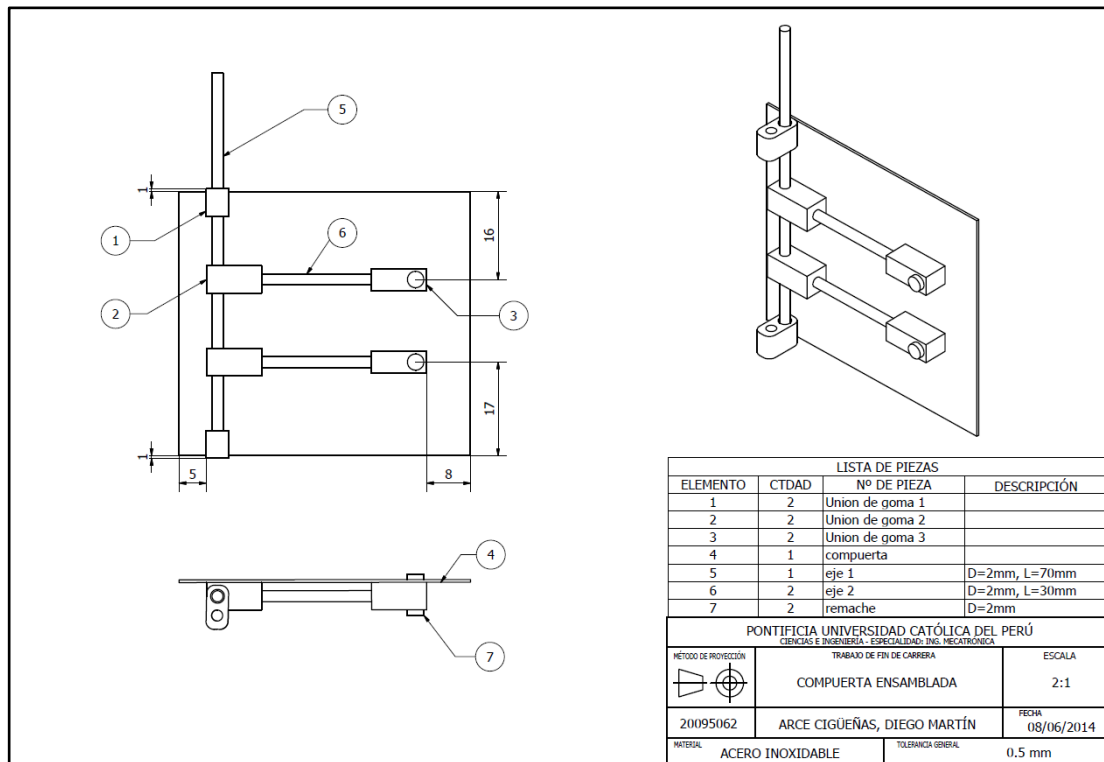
Plano de ensamblaje *Compuerta ensamblada*.
